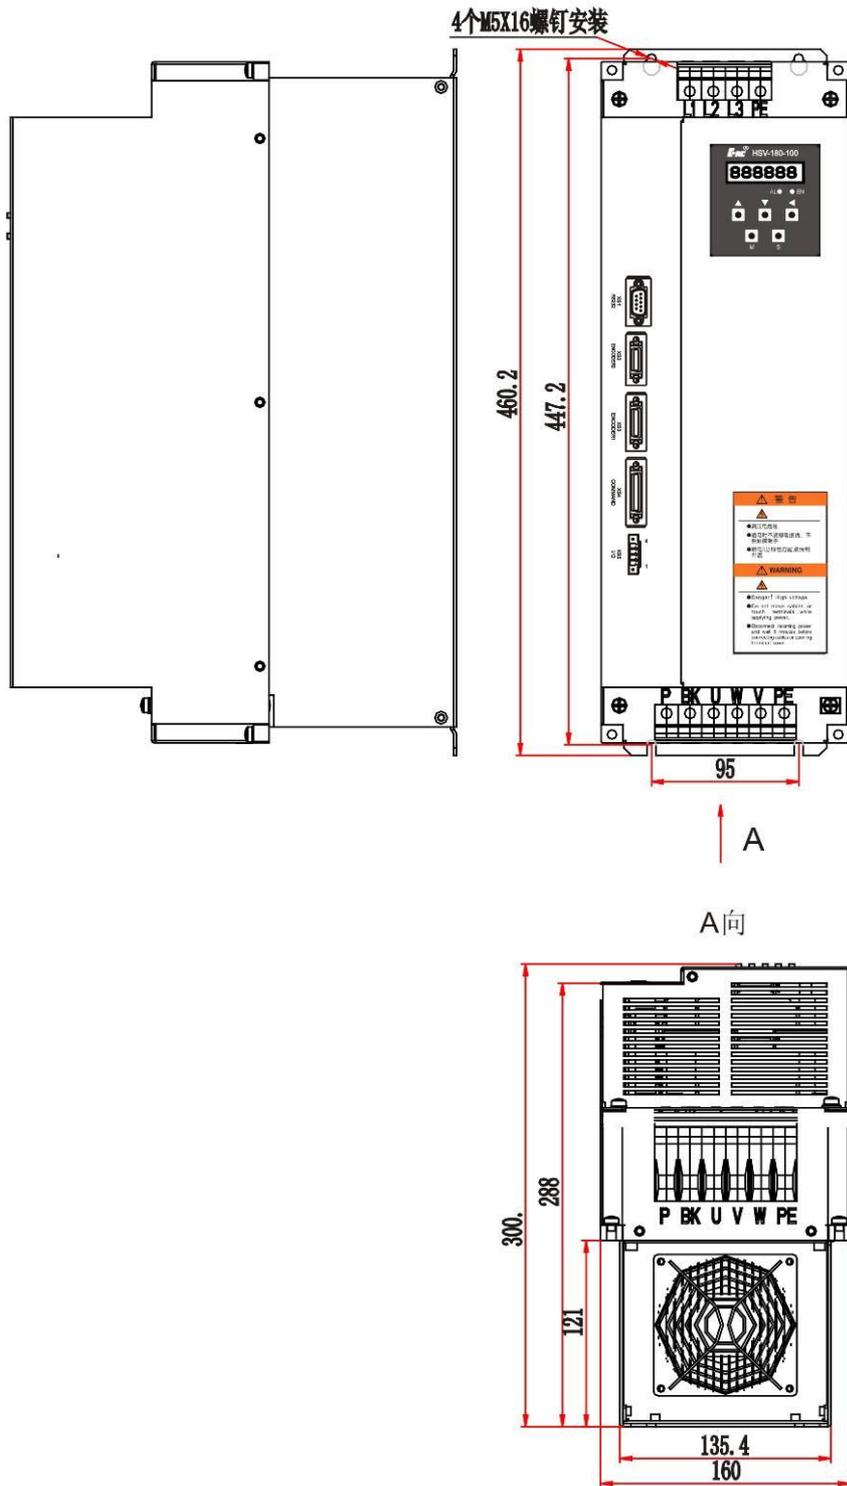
HSV-180AD-100, 150 伺服驱动单元外形尺寸（带辅助安装装置 单位：mm）
